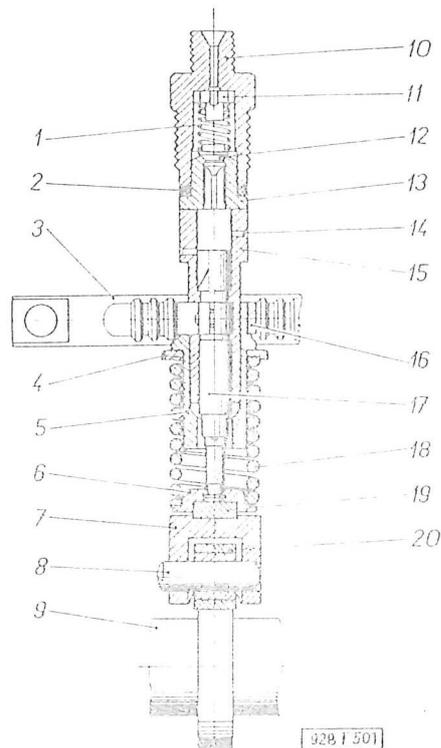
Schnitt durch die Einspritzeinheit (Pumpenelement)
